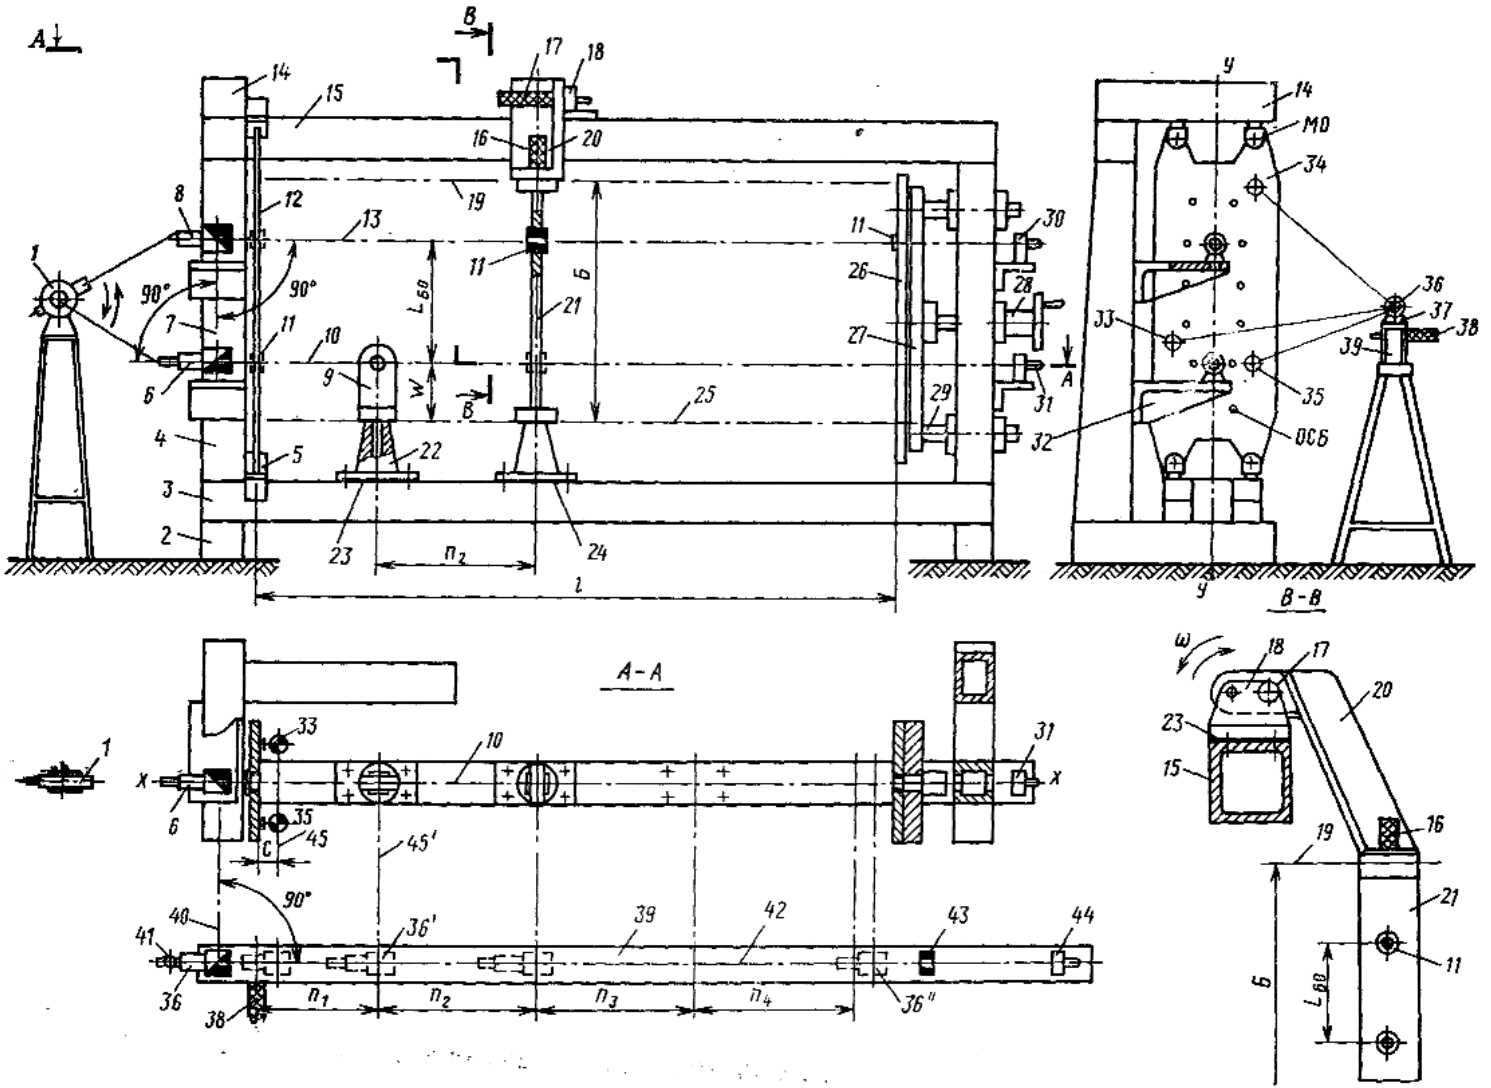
Координатная система и схема установки оптических приборов при монтаже приспособления для сборки центрального (см. рис. 1.17):
